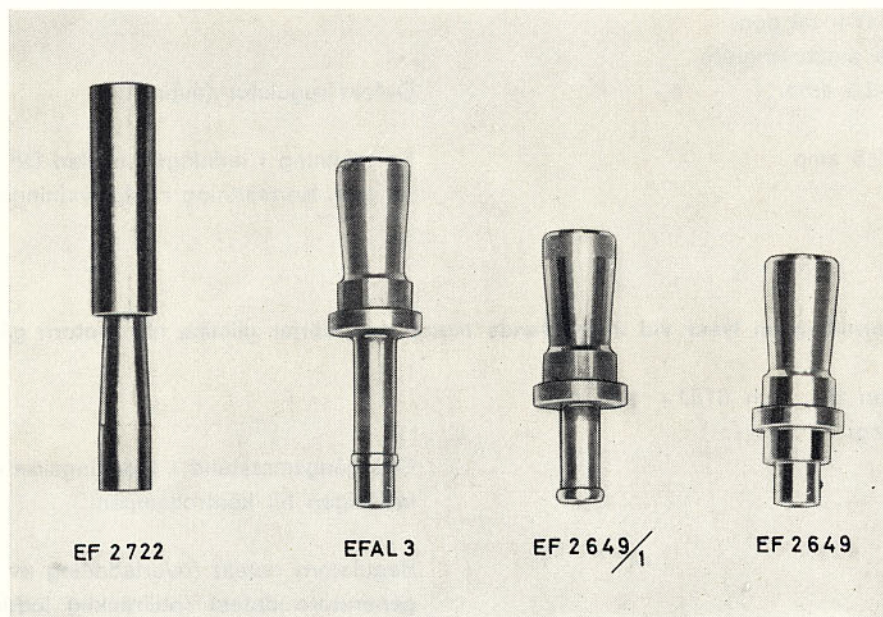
Bosch specialverktyg för startmotor (sen. utf.)
